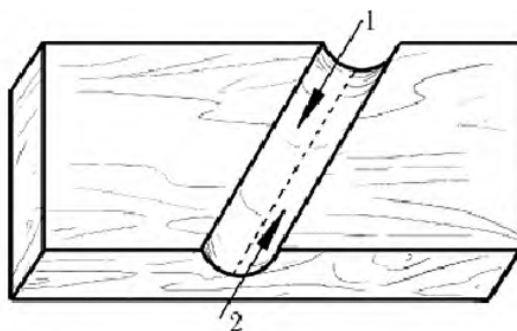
Выполнение полукруглой выемки, которая расположена на заготовке наклонно (стрелками показано направление движения инструмента)
